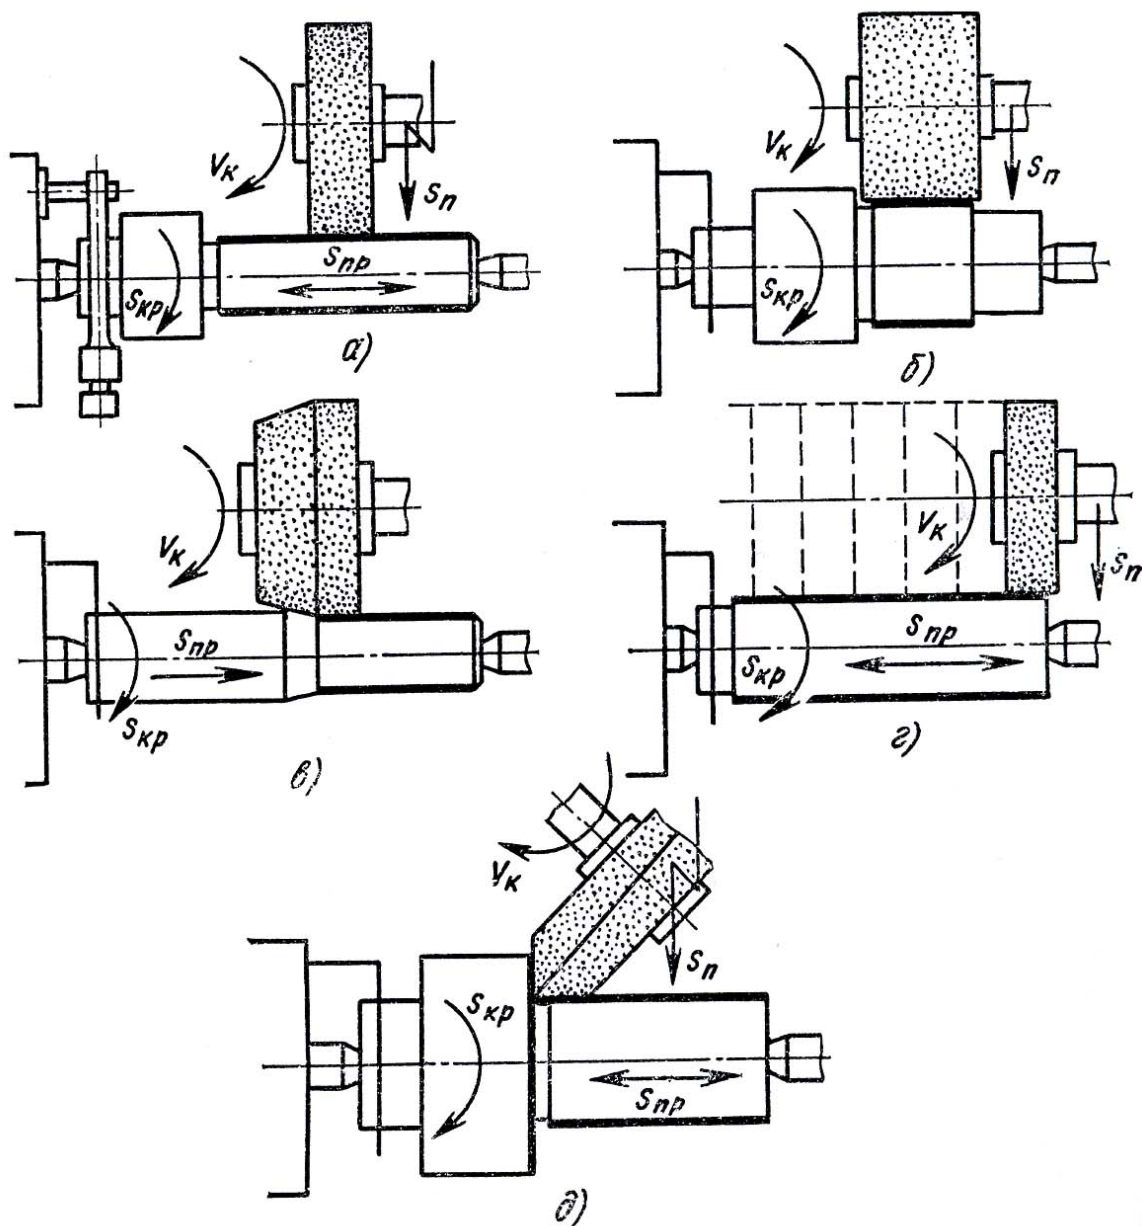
Схемы обработки заготовок на круглошлифовальных станках:
